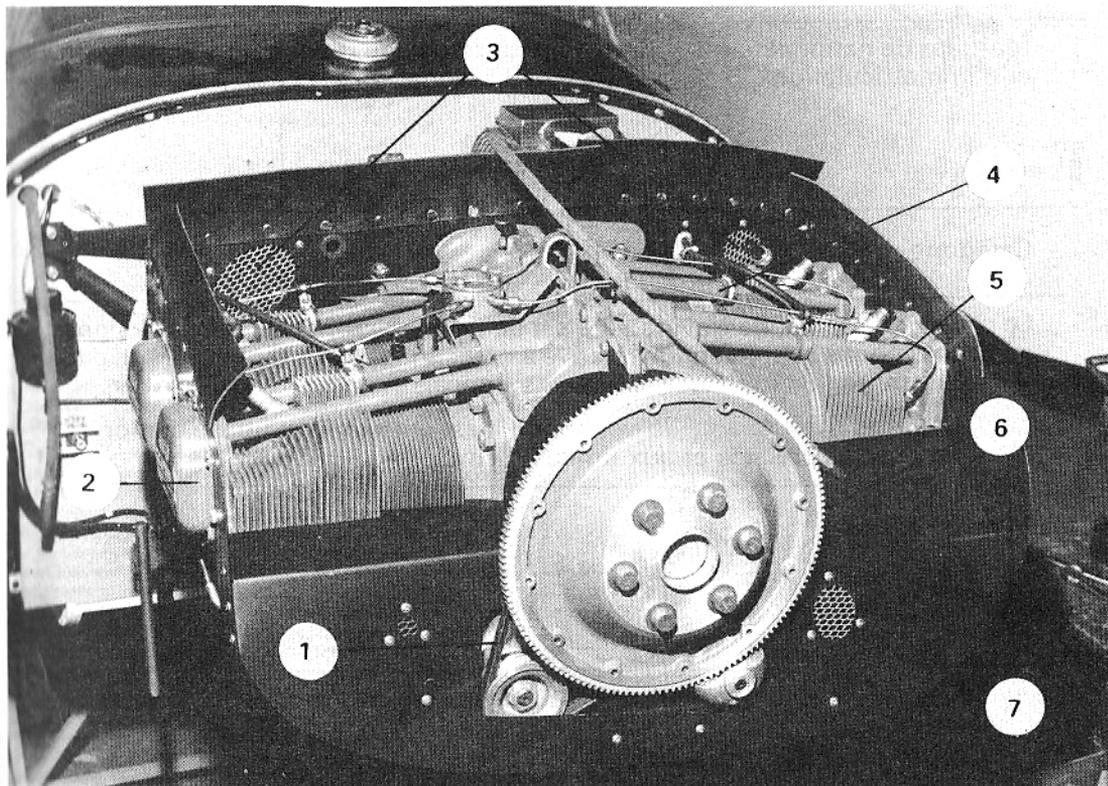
Moteur à injection 180 ch monté sur bâti en tubes d'acier soudés.
